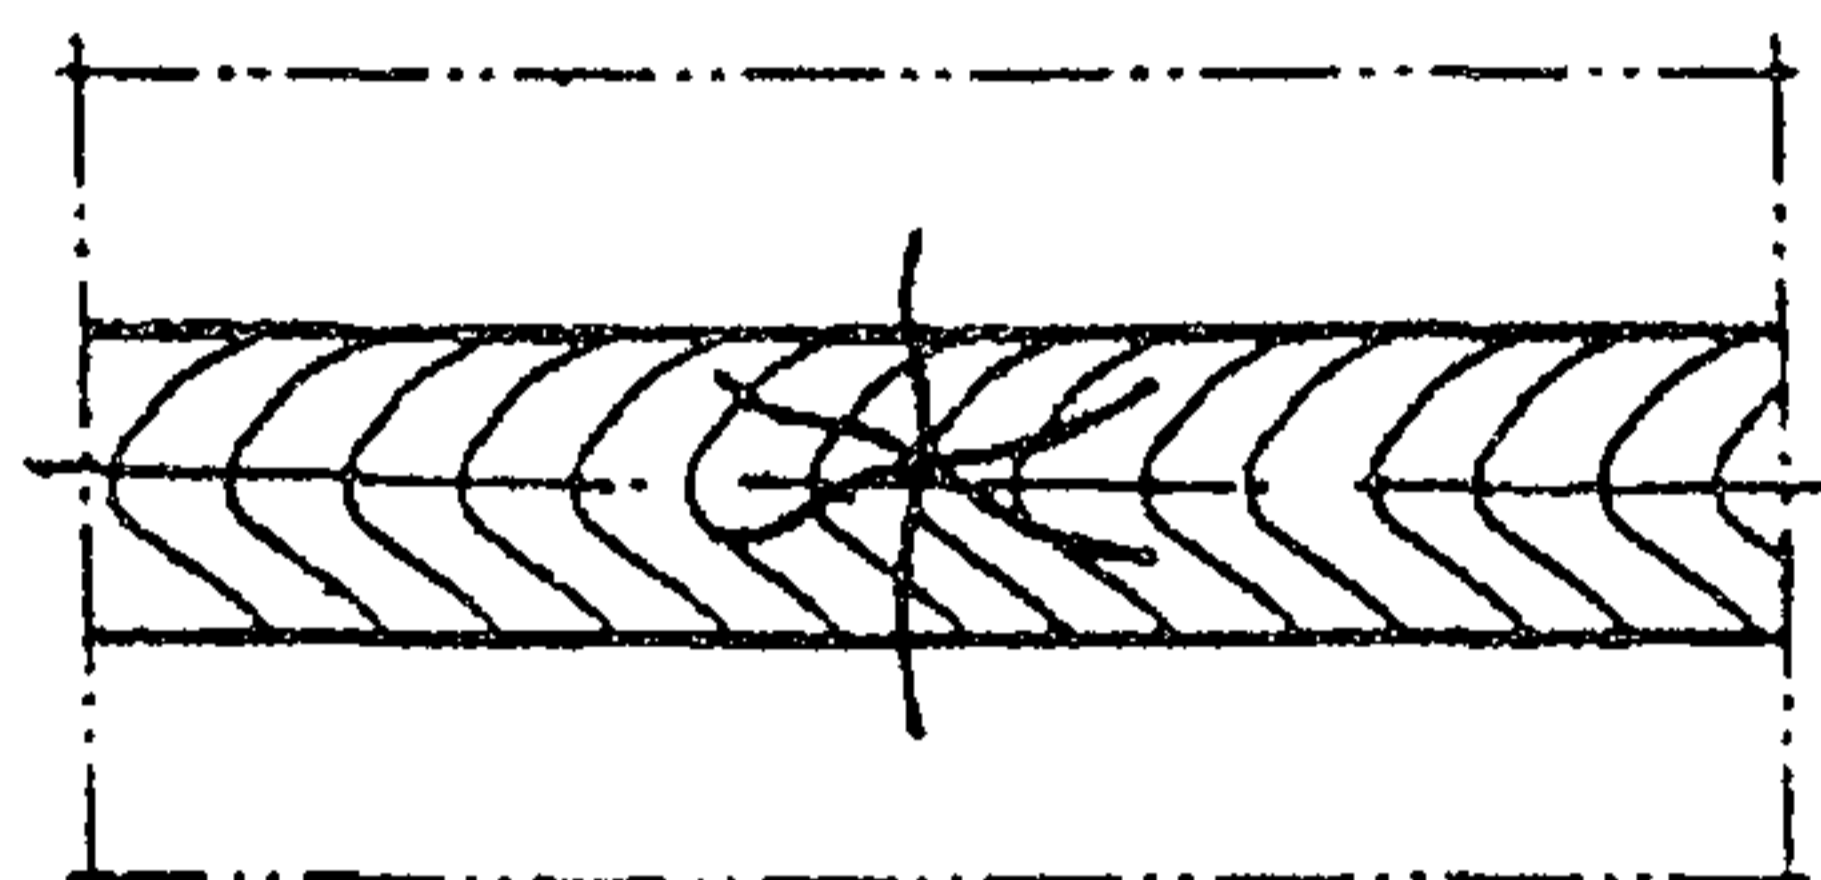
Радиальные трещины сварного соединения
